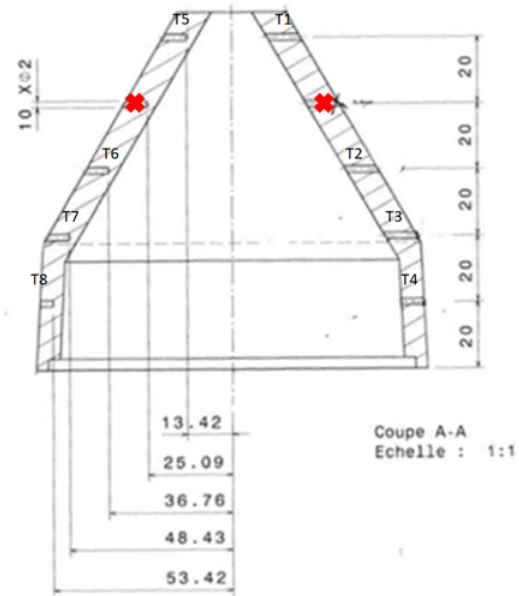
Dessin d'ensemble du moule Tatur
